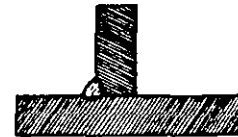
Símbolo de soldadura de acanaladura U y la soldadura correspondiente que se desea obtener.
